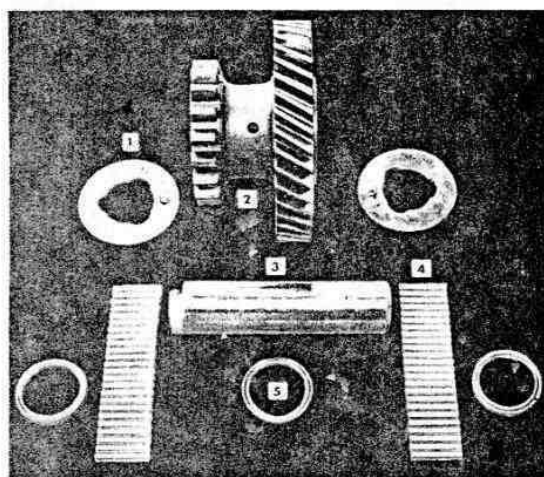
Conjunto del engranaje intermedio de la Caja de Transferencia. 1) Arandela de empuje. 2) Engranaje intermedio. 3) Eje del engranaje intermedio. 4) Rodillos del cojinete del engranaje intermedio. 5) Arandelas espaciadoras del cojinete.
